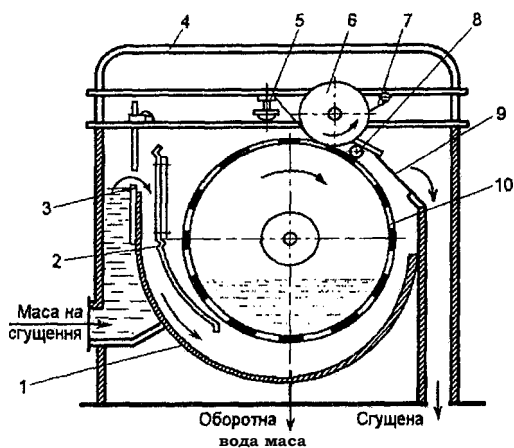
Згущувач шаберний: 1 - ванна; 2 - заспокоюючий щит; 3 - регулювальний щит; 4 - ковпак; 5 - механізм притиску шаберного валика; 6 - шаберний валик; 7 - шабер; 8 - спорск; 9 — похилий щит; 10- циліндр
